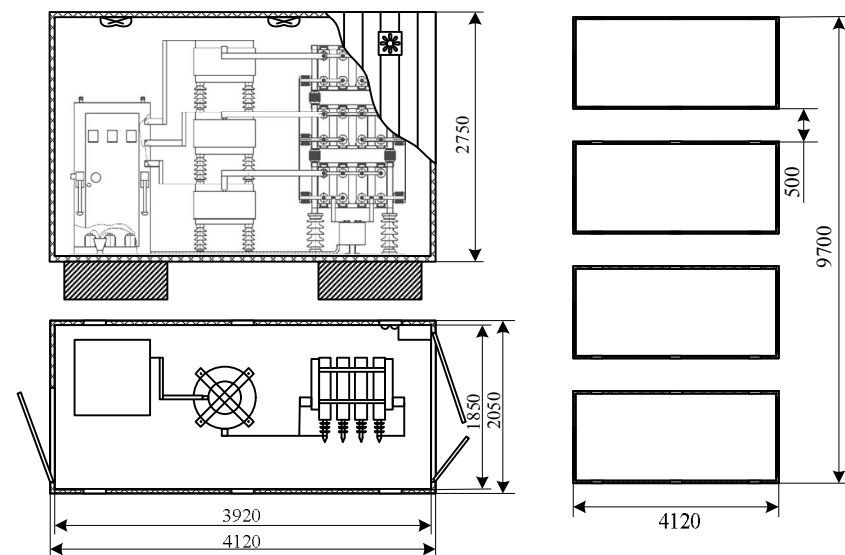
Габаритне креслення боксу з ФКП та площадки, яку будуть займати установки для фільтрації 5, 7, 11 та 13 гармонік
